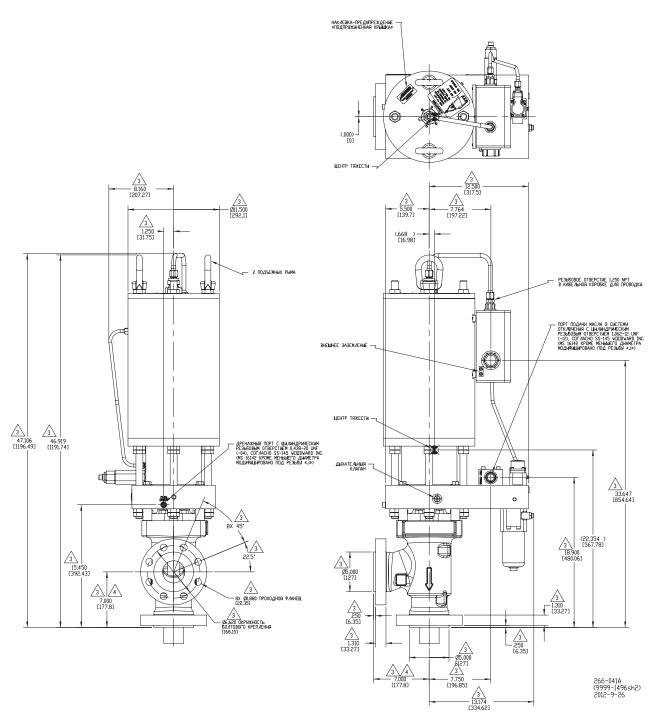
а. Габаритный чертеж регулятора SonicFlo (3 дюйма, класс 600)
